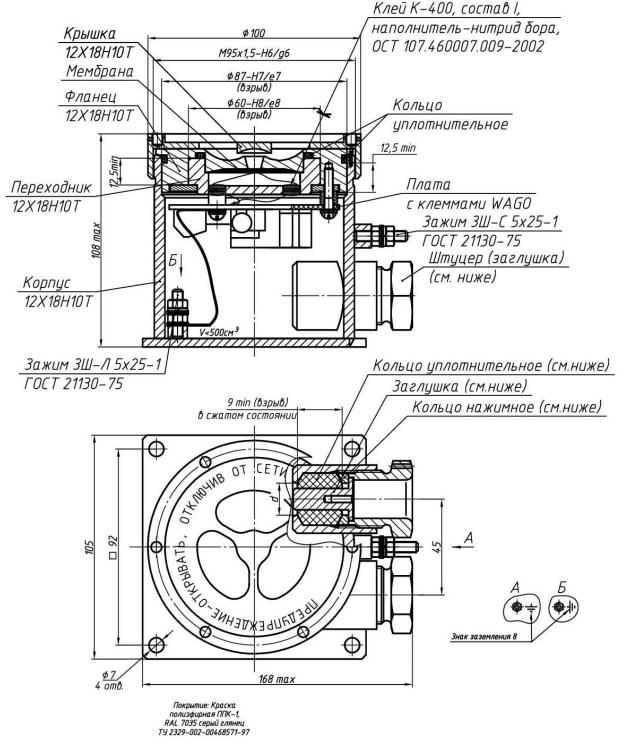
Габаритный чертёж звуковых оповещателей моделей ЕхОППЗ-2В-Н, ЕхОППЗ-2В-220-Н в корпусе из нержавеющей стали, совмещённый с чертежом взрывозащиты. Маркировка показана в п. 1.6
